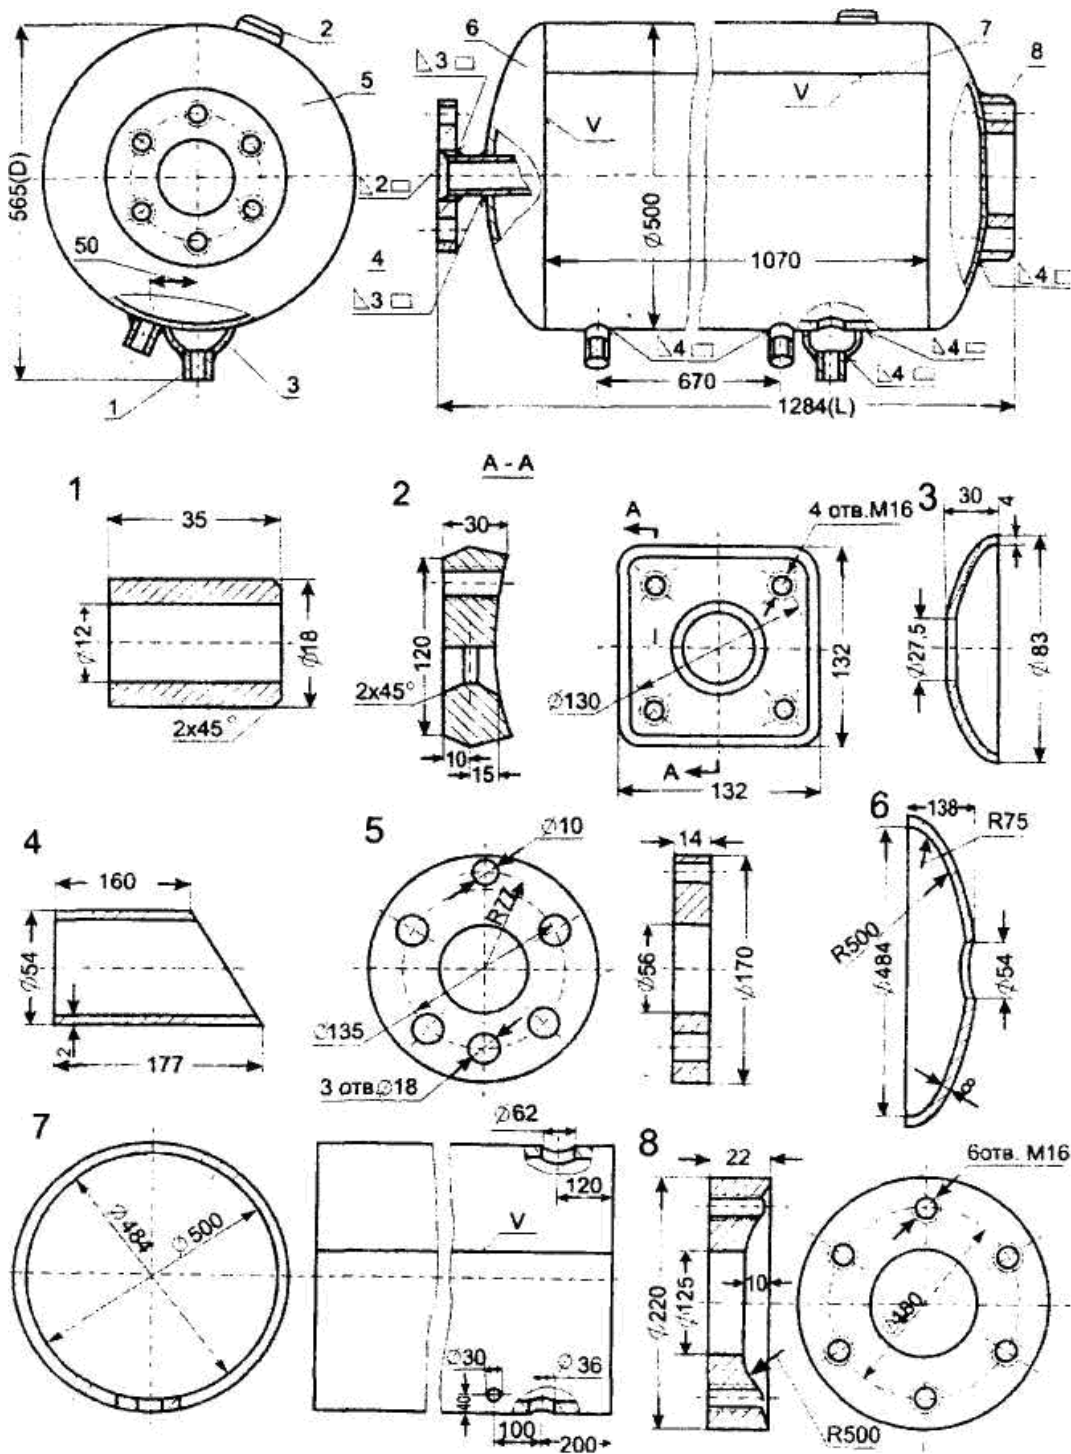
Эскиз корпуса воздухоборника и его деталей для задания № 11
